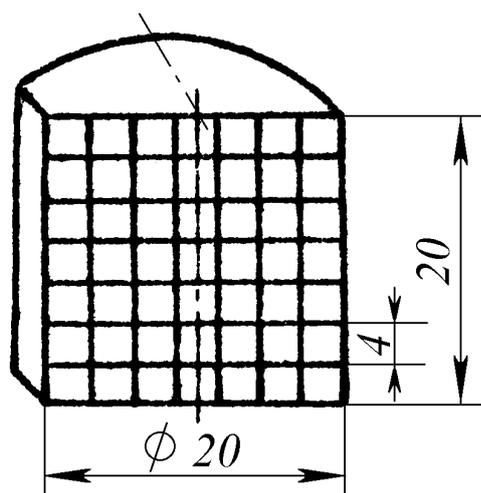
Половина заготовки для прессования с нанесенной координатной сеткой
